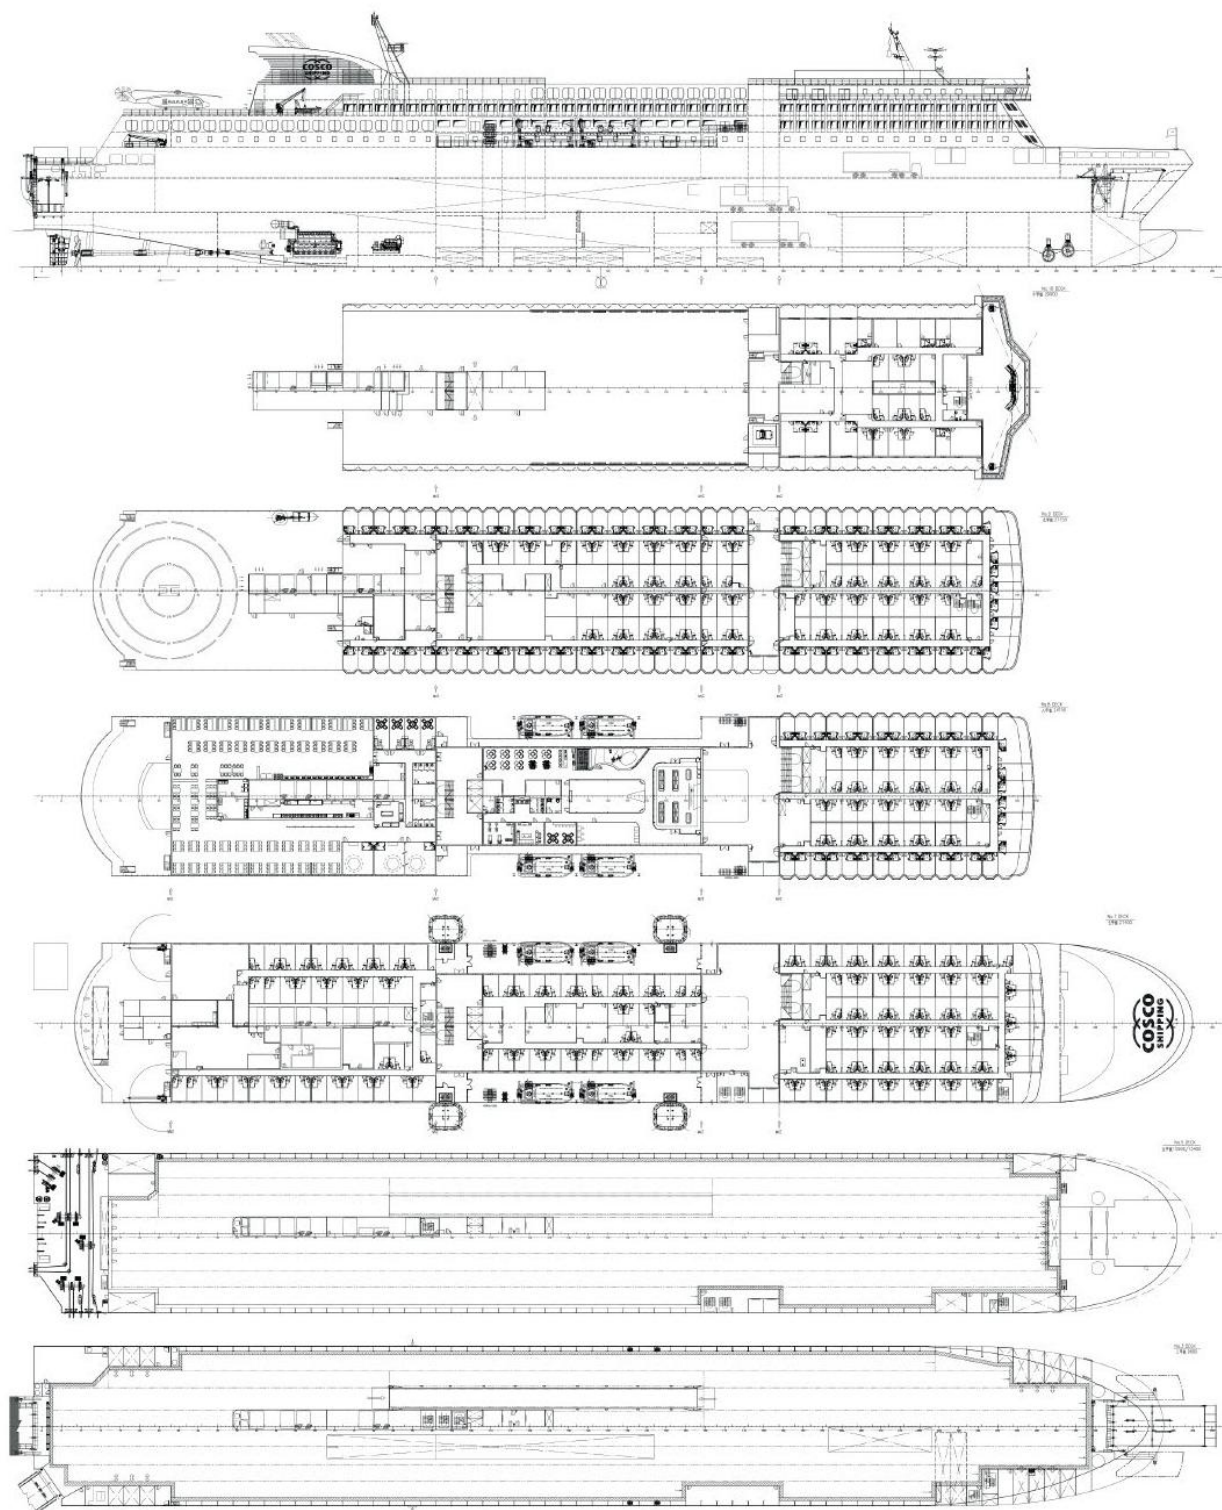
Поперечні та повздовжні перерізи парома Ji Long Dao
